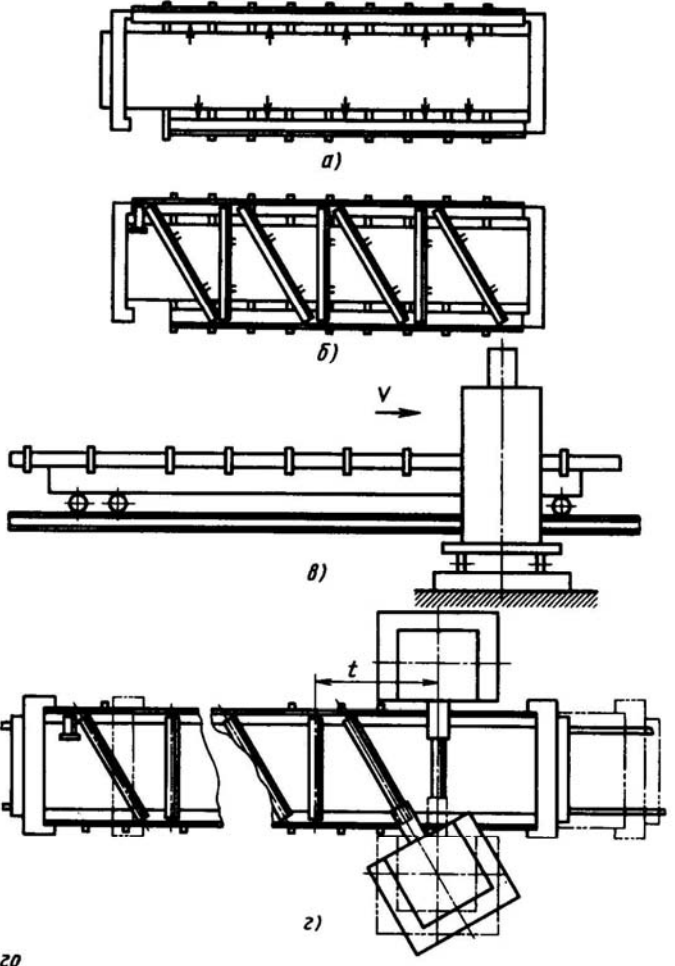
Последовательность сборочно-сварочных операций
